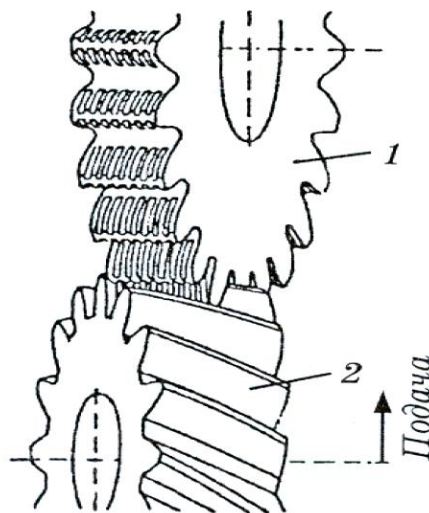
Шевингование зубьев зубчатым шевером: 1 – шевер; 2 – обрабатываемое зубчатое колесо
